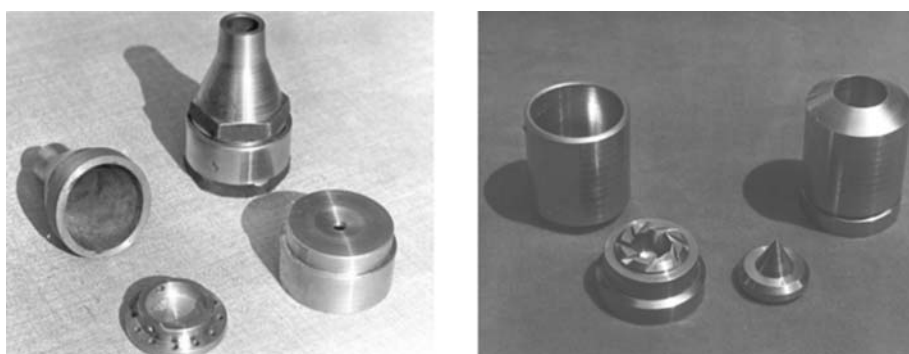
Детали мазутных форсунок различных конструкций после механической обработки. Изготовлены литьем по выплавляемым моделям
